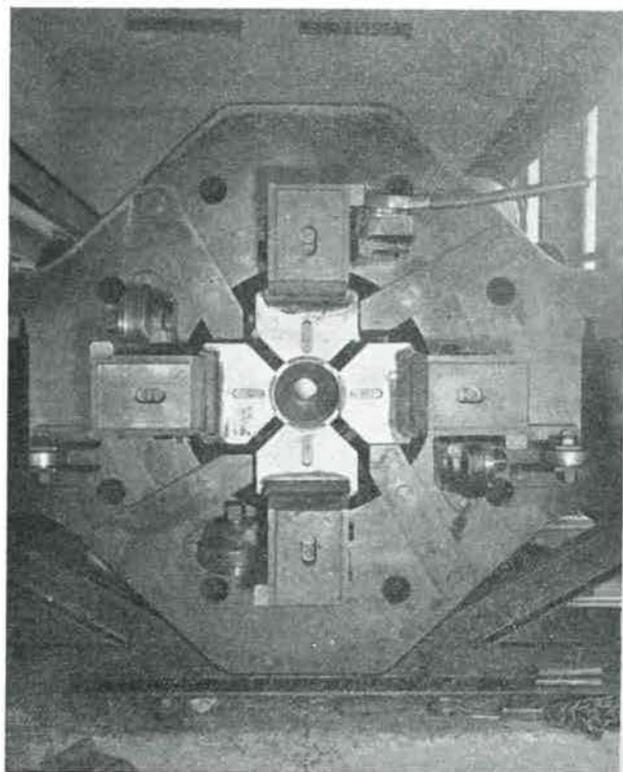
Vue des coins avec leur garniture de fourrures coniques montées sur la machine.
